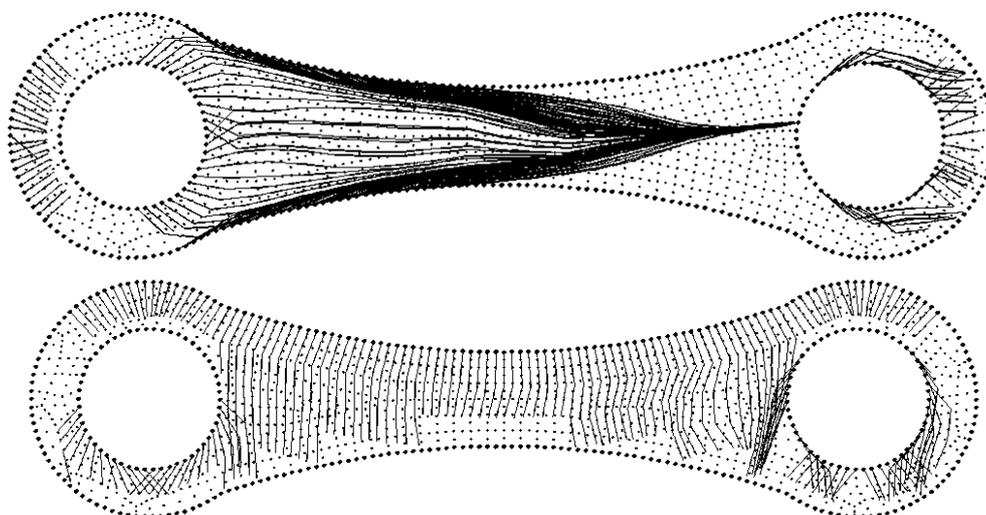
Кривые укладки нитей армирующего наполнителя для детали, работающей на изгиб. а – в четных слоях, б – в нечетных слоях.
